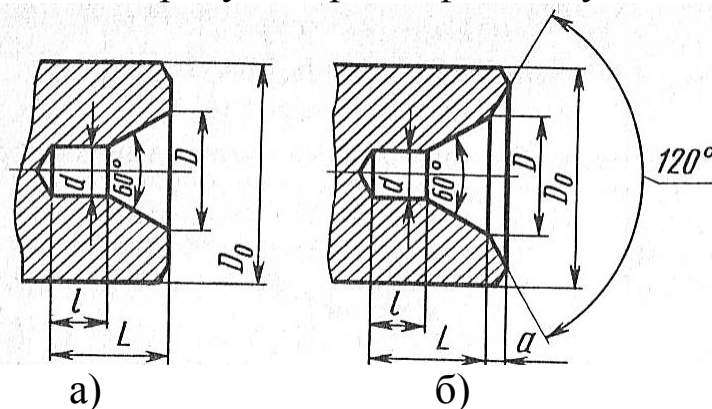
Центровые отверстия: а – без предохранительной фаски; б – с предохранительной фаской;  $d$  – диаметр свела;  $D$  – наружный диаметр сверла;  $l$  – глубина цилиндрического отверстия (углубление);  $L$  – длина отверстия;  $D_0$  – диаметр заготовки;  $a$  – глубина фаски
